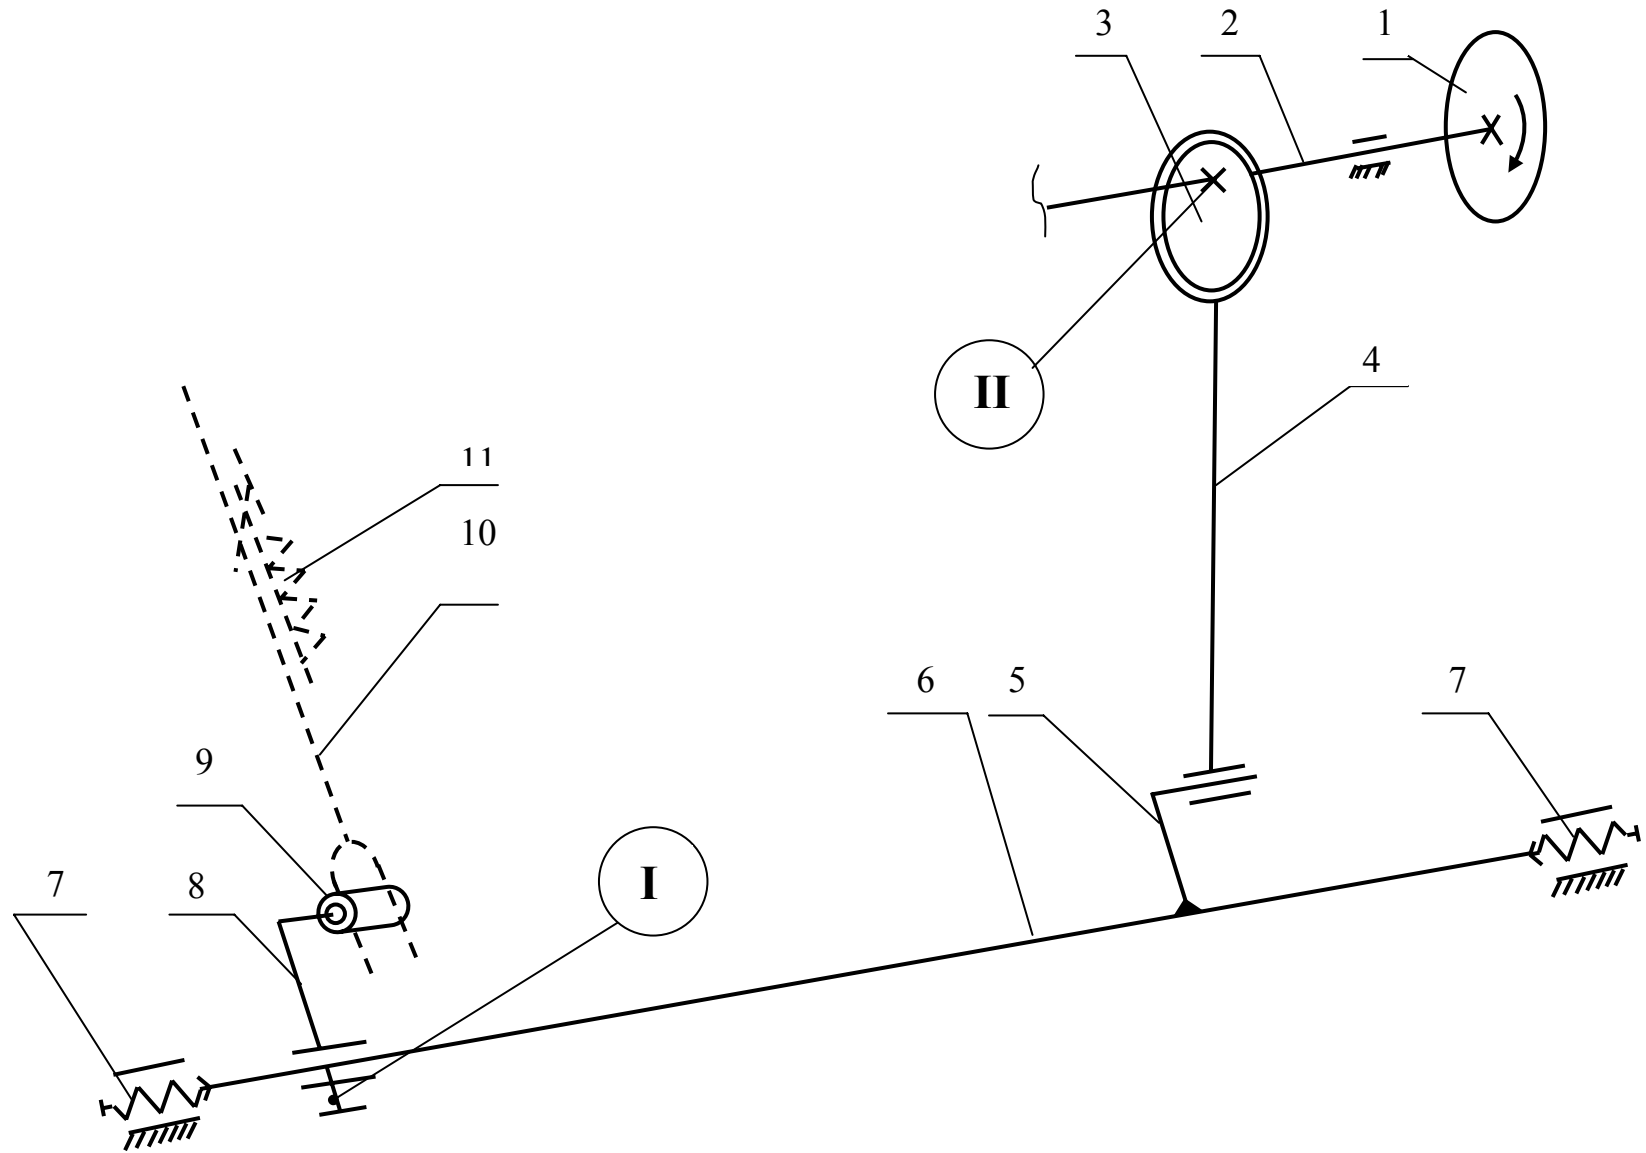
Кинематическая цепь подъема зубчатой рейки механизма перемещения материала
